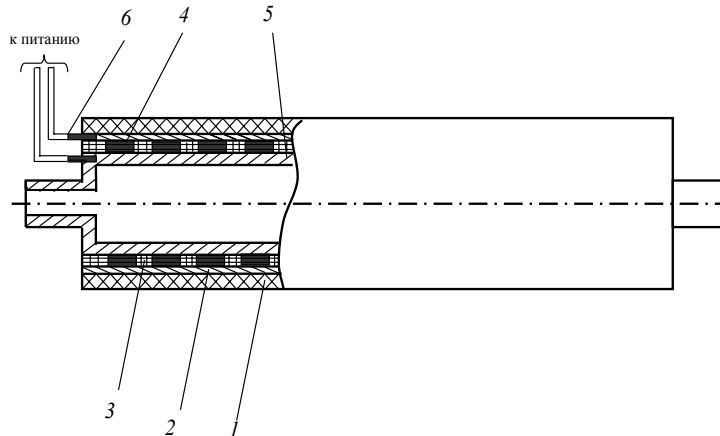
Схема лабораторного образца саморегулируемого устройства электроподогрева двигателя (СУЭД)
